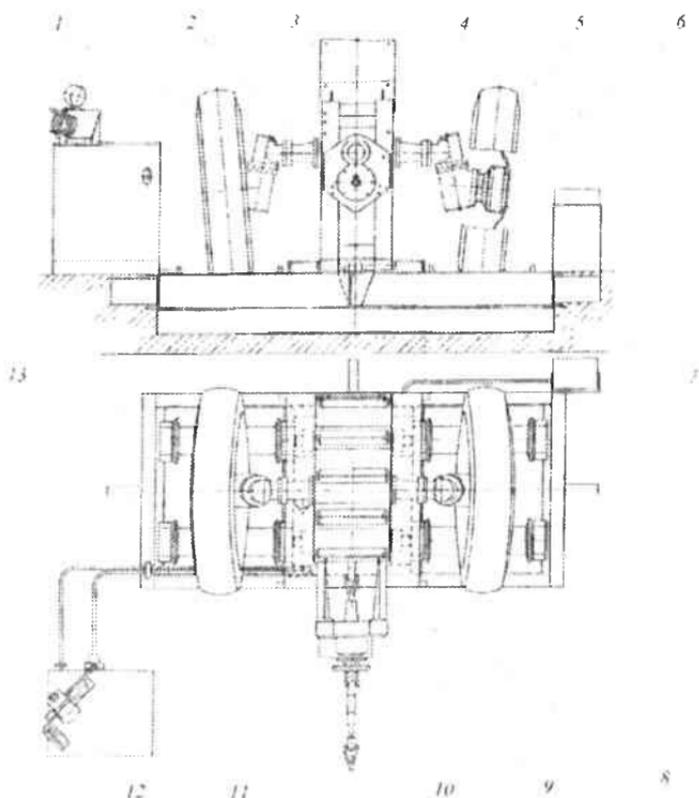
Стенд для испытания переднего моста: 1 – повышающий редуктор; 2 – передний мост; 3 – балластные грузы; 4 – приспособления для установки испытываемого объекта; 5 – колесо; 6 – проставка; 7 – рама; 8, 12 – лонжероны; 9, 11 – карданные валы; 10 – ВОМ трактора; 13 – беговые ролики
